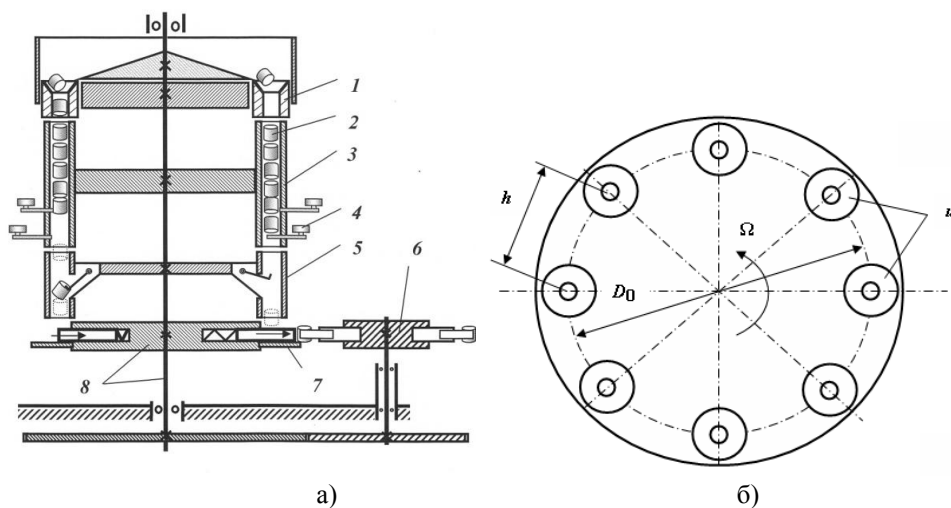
Типовая схема роторной САЗ однороторной компоновки: а – продольный разрез; б – вид сверху; 1 – вращающаяся воронка; 2 – предмет обработки; 3 – накопитель; 4 – механизм поштучной выдачи; 5 – ориентатор; 6 – транспортный ротор; 7 – шиберный питатель; 8 – транспортно-несущее устройство
